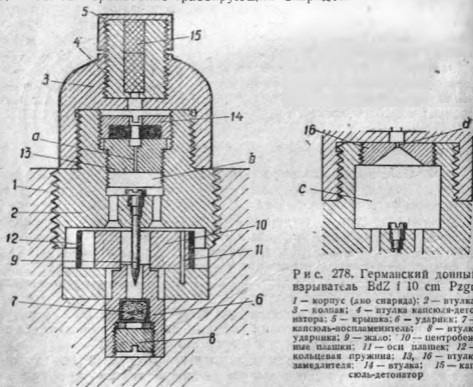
Германский донный взрыватель BdZ f 10 cm Pzgr: 1 — корпус (дно снаряда); 2 — втулка; 3 — волнак; 4 — втулка капсуля-детонатора; 5 — крышка; 6 — ударник; 7 — капсуль-воспламенитель; 8 — втулка ударника; 9 — жало; 10 — центробежные пашки; 11 — оси пашек; 12 — кольцевая пружина; 13, 16 — втулка замедлителя; 14 — втулка; 15 — капсуль-детонатор
